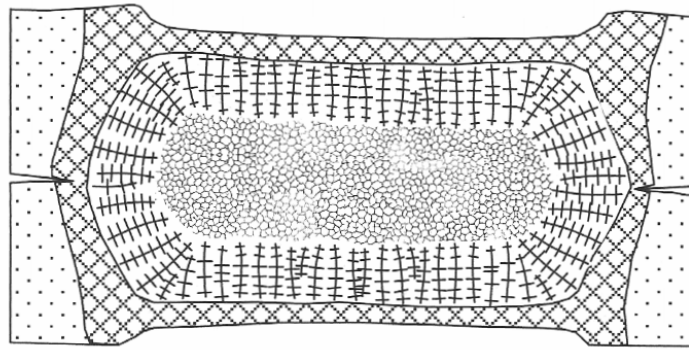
22. Estructura esquemática de un punto de soldadura ideal<sup>24</sup>
